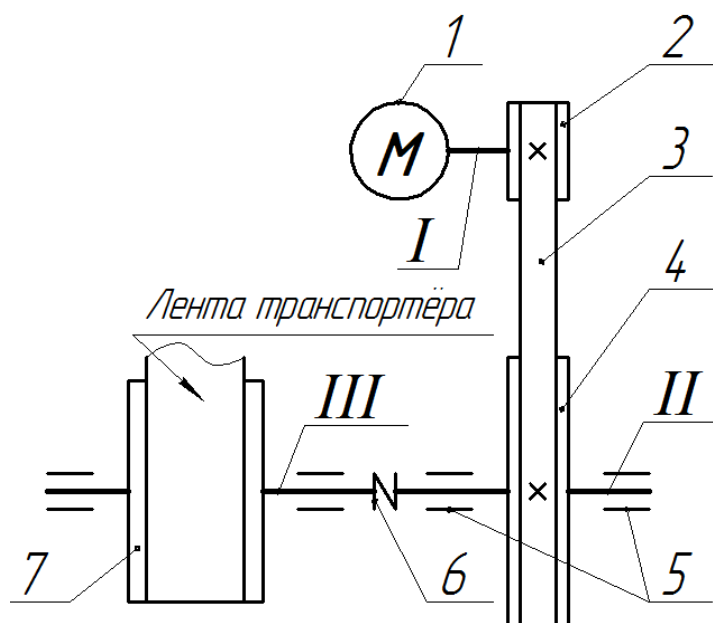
Схема привода: 1 – электродвигатель; 2 – шкив ведущий; 3 – ремень; 4 – шкив ведомый; 5 – подшипники; 6 – муфта соединительная; 7 – барабан транспортера.
